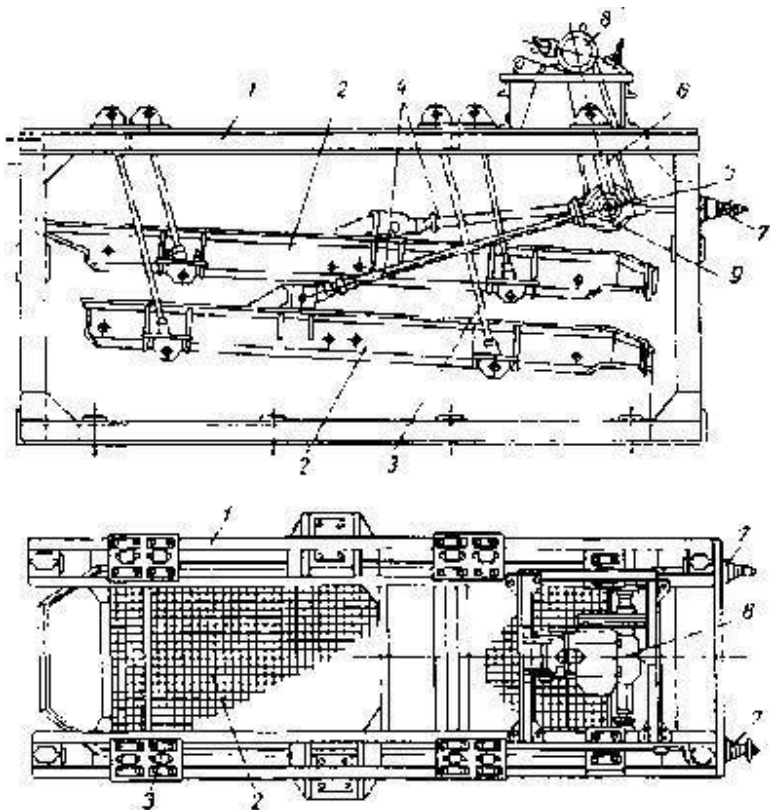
Общий вид быстроходного качающегося грохота типа БКГ
